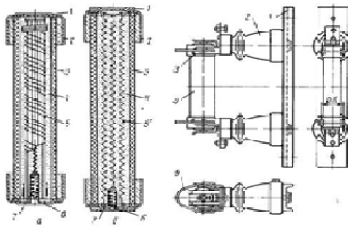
А: патроны предохранителей типа ПКТ: 1-на номинальные токи до 7.5 А; 2-на номинальные токи 10...400А; б) 1 крышки; 2-латунный колпачок; 3 фаянсовая трубка; 4-кварцевый песок; 5 и 5-плавкие вставки; 6 указатель срабатывания; 7-пружина.
